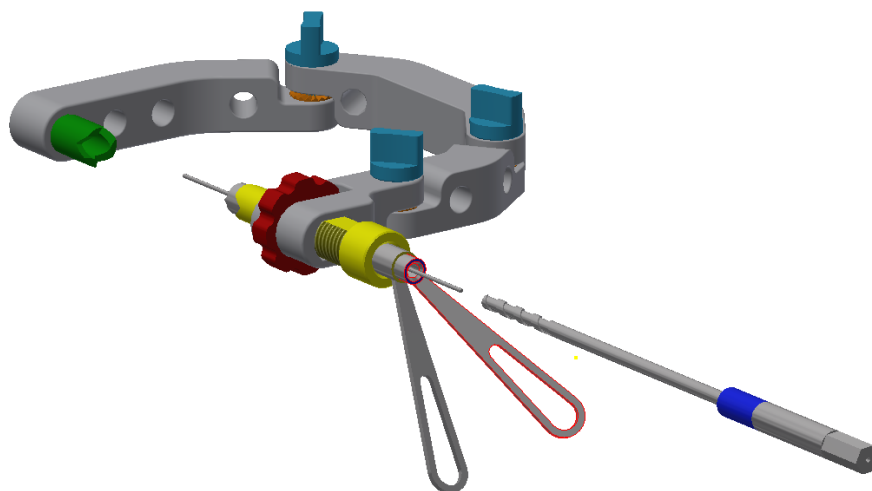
Detail vrtacího pouzdra pro K-drát
